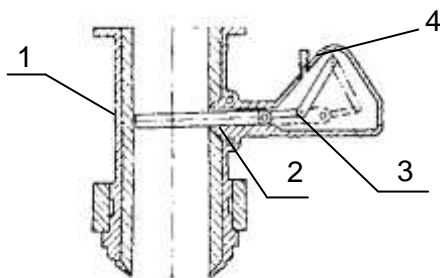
Шиберное устройство для регулирования расхода дутья через фурму печи: 1 – неподвижный патрубок; 2 – шибер; 3 – рычаг; 4 – кожух
